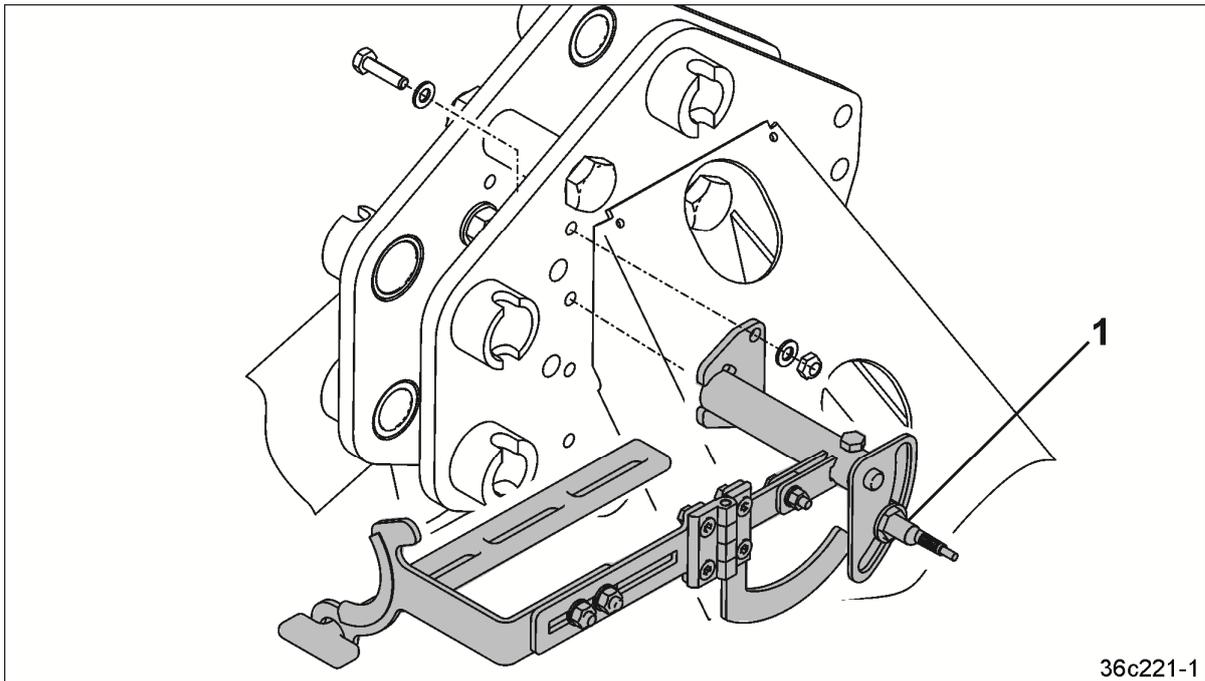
Fije el sensor de posición de trabajo digital (Fig. 103/1), mediante las instrucciones de montaje enviadas, al punto de acoplamiento superior de la máquina de labranza.
